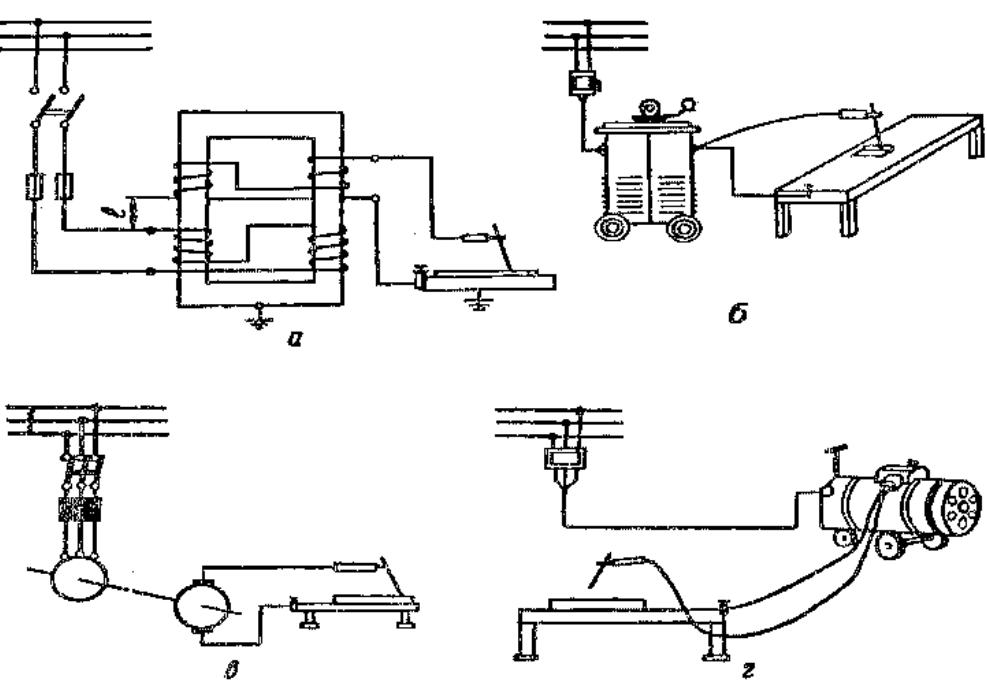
Схемы сварочных постов для ручной сварки
